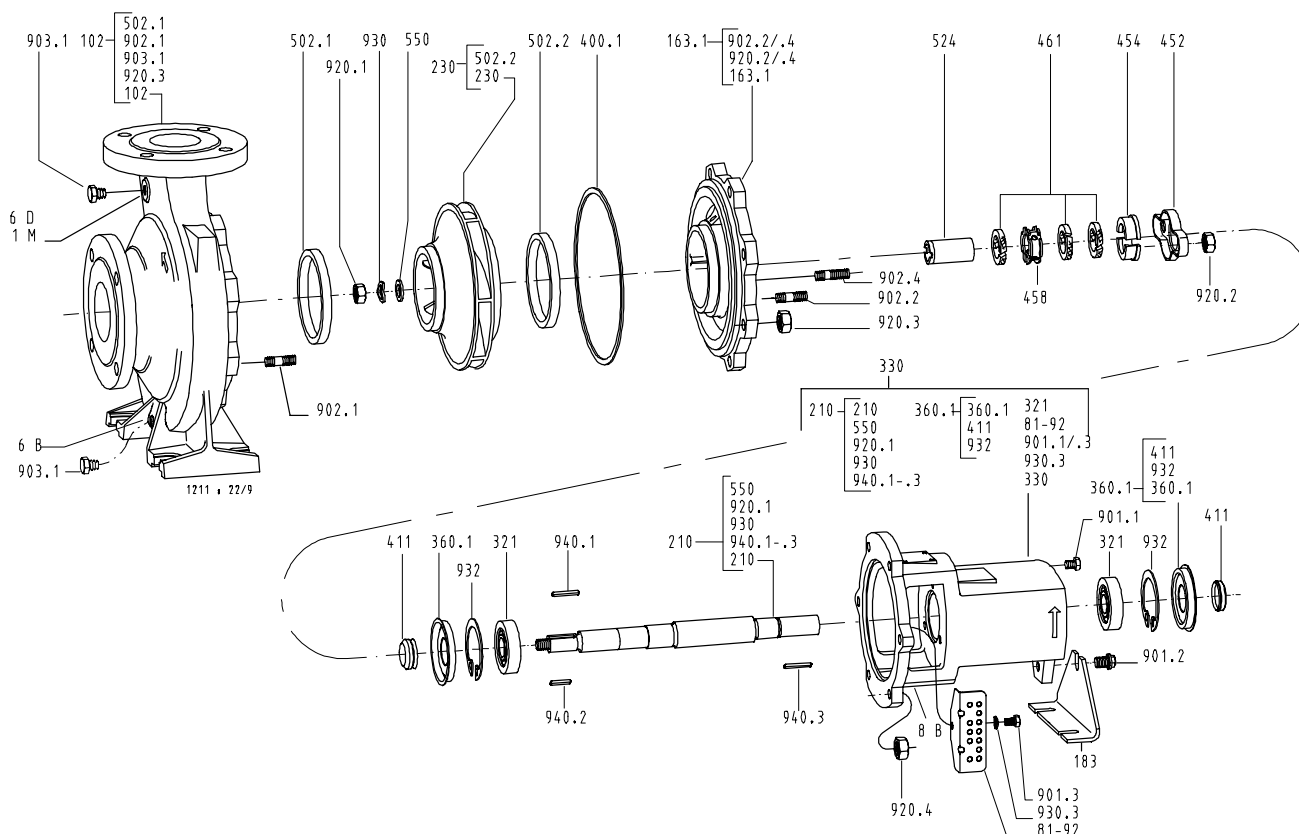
Сальниковая набивка и резьбовая напорная крышка
